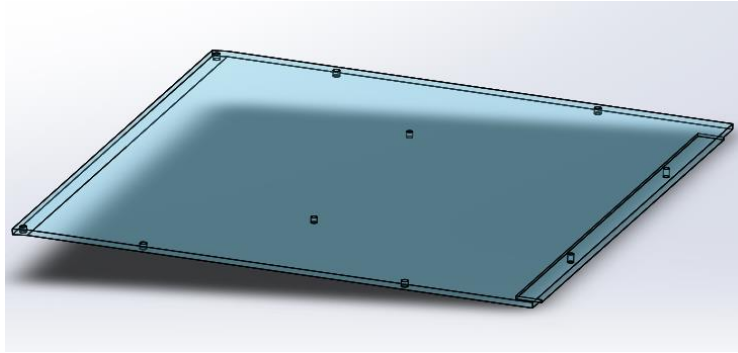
Vista de una de las placas de la cubierta. Fuente: Propia.
